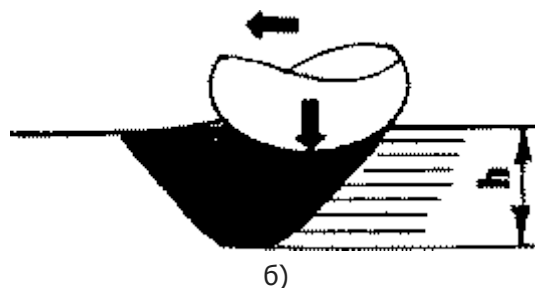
Схема обработки детали алмазным выглаживанием
